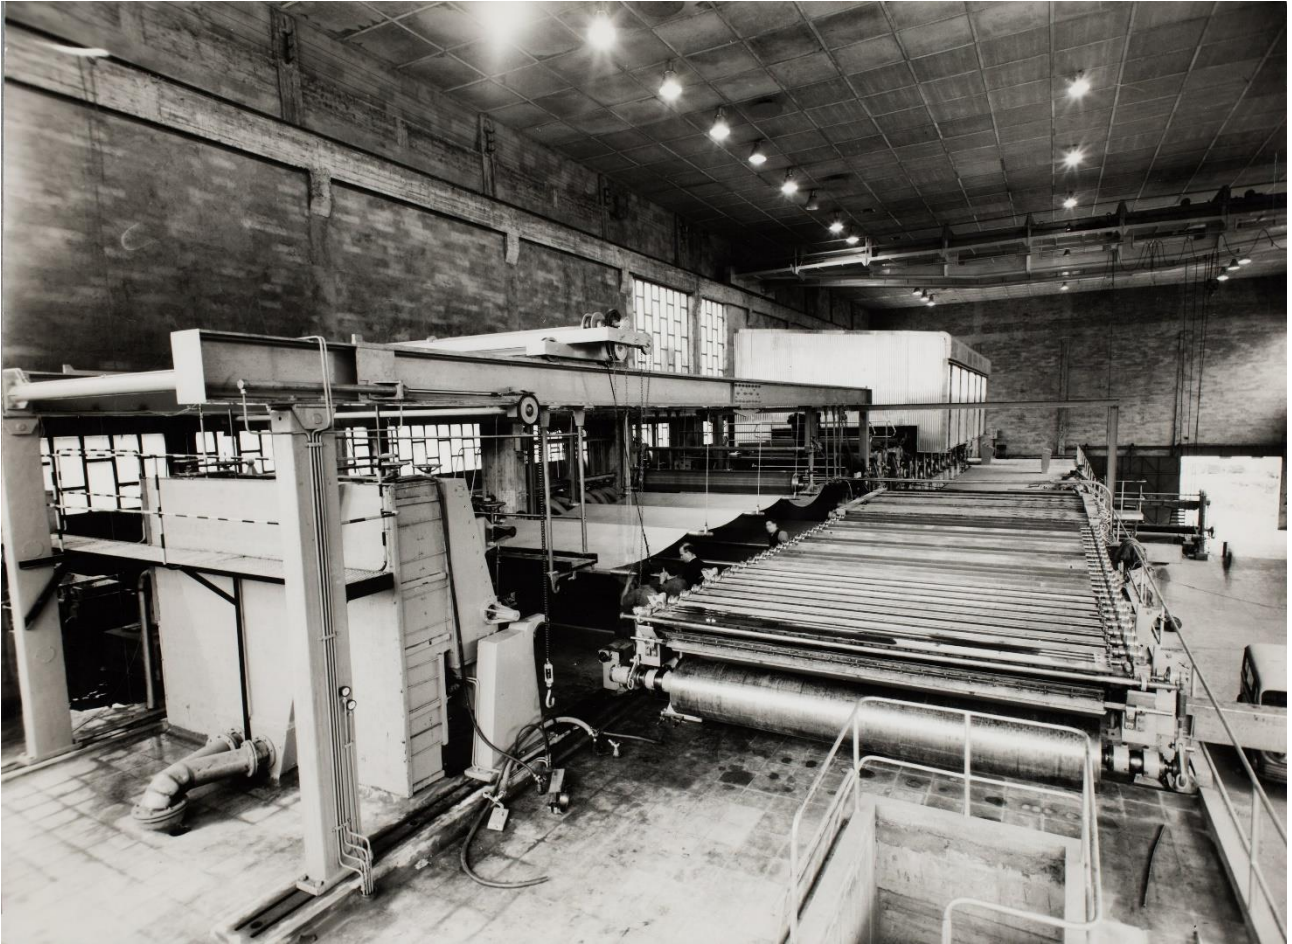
Interior del nuevo pabellón. (AEPE F 697)
